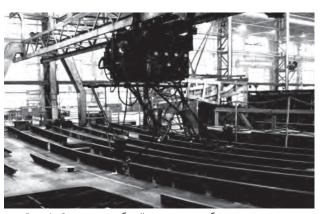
Сварка палубной секции корабля шланговыми автоматами ПШ-5
